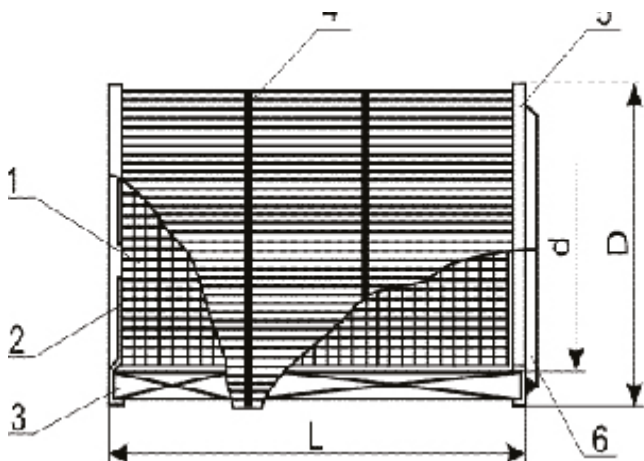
Схема патронного фильтрующего элемента. 1 - опорная сетка; 2 - металлический концевой диск; 3 — миниплиссированный фильтрующий пакет; 4 - бандажный пояс; 5 - концевое кольцо;
